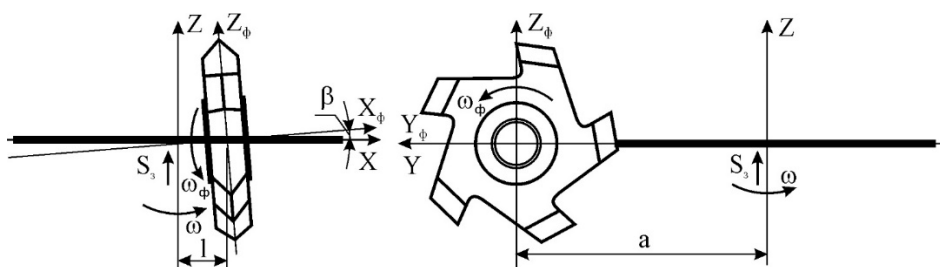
Схема движений обкаточной фрезы и заготовки фрезы
